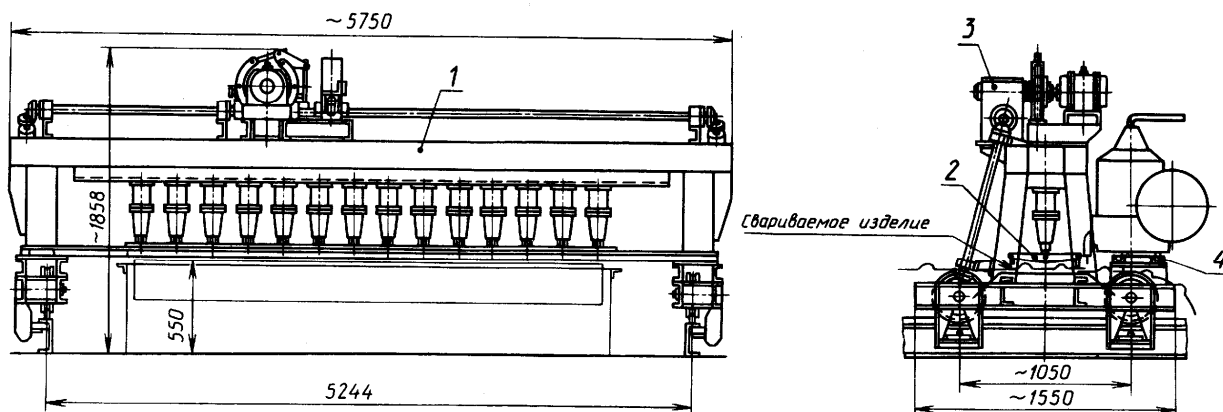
Самоходный портал с прижимной траверсой для сварки прямолинейных швов
